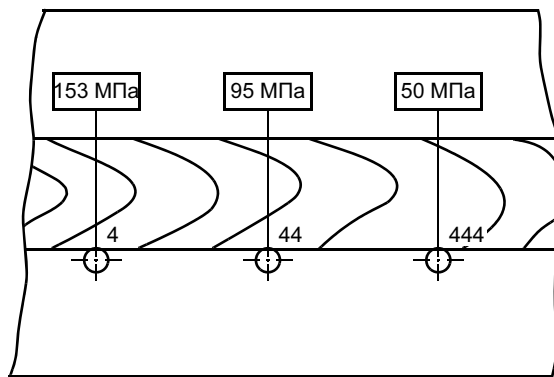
Напряжения в точках 4, 44 и 444, расположенных на линии сплавления сварного соединения
